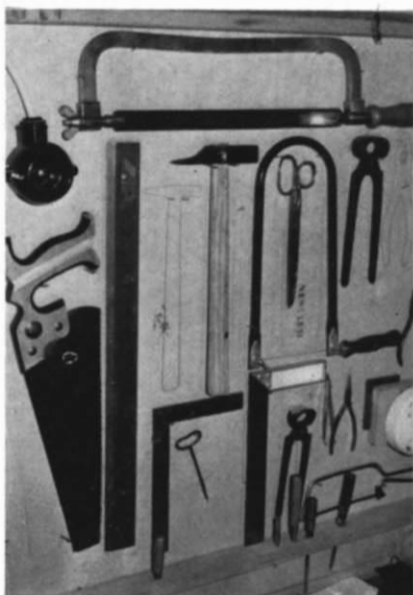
Angesichts solch „griffgerechter“ Werkzeugaufhängung, durch die zudem so gut wie keine Grundfläche beansprucht wird, kann die Arbeit geradezu zum Vergnügen werden.
